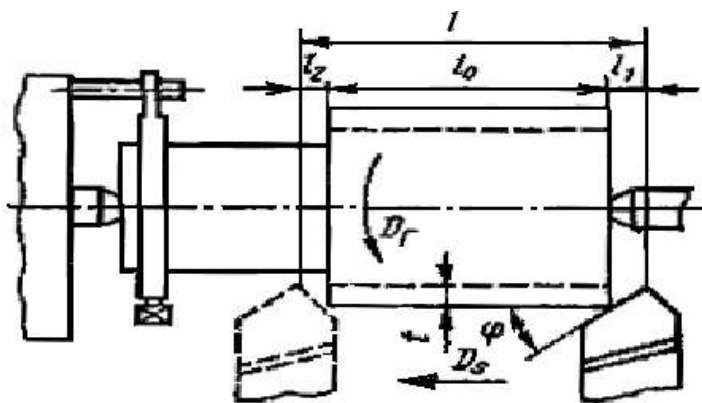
Схема к расчёту T_0 при обработке цилиндрической поверхности
